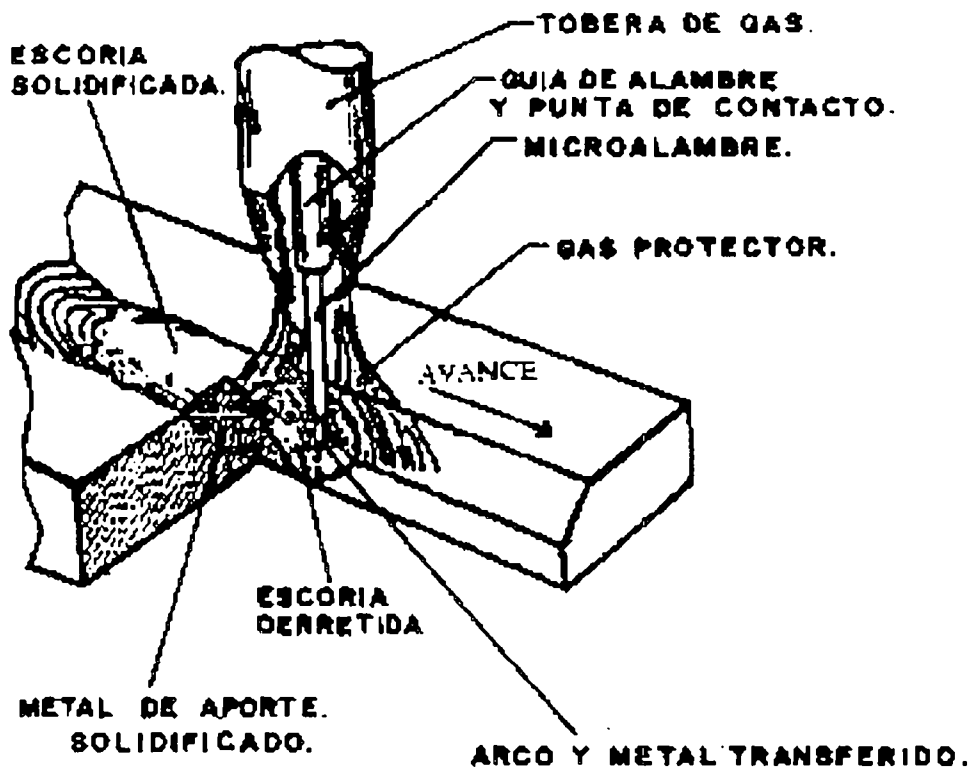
Esquema de proceso de soldadura GMAW.
